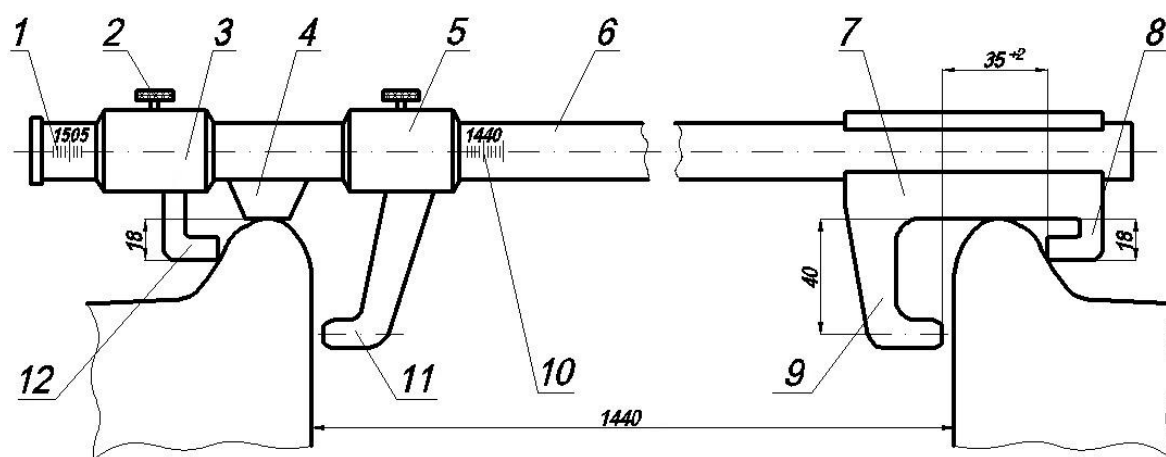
Штанген для вимірювання відстані між поверхнями коліс колісної пари
